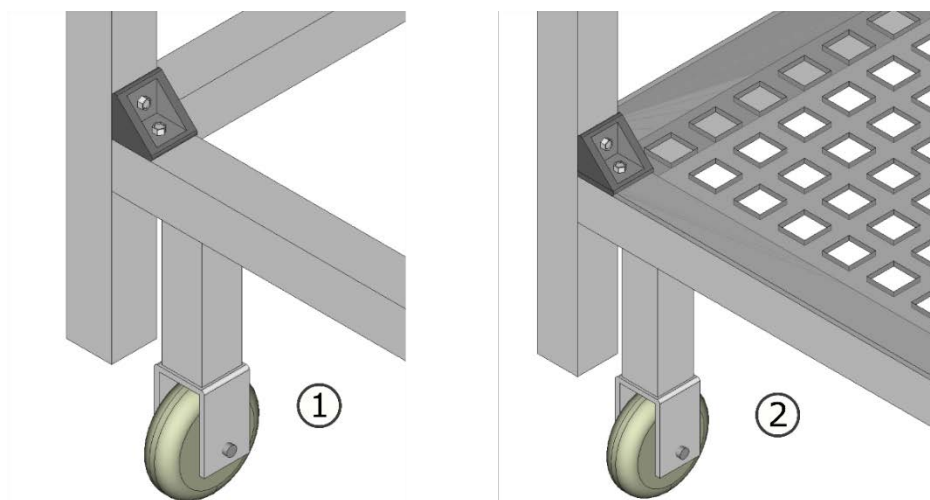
Montaje del armazón de la instalación. Fuente: Elaboración propia.
